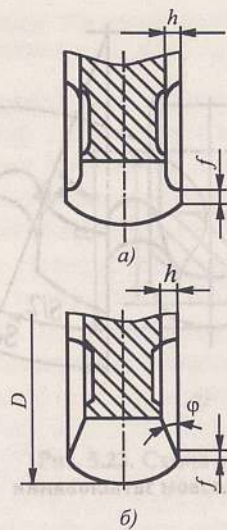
Профиль зубьев фрез для обработки глубоких пазов
